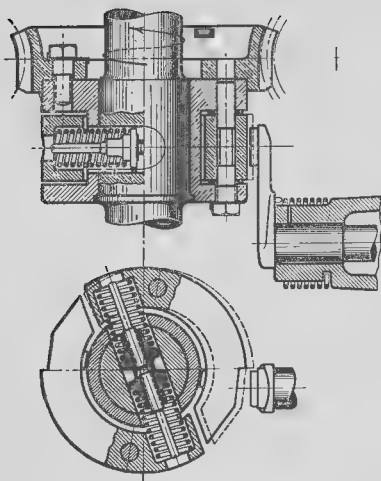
Предохранительный выключатель турбины Броун-Бовери.
